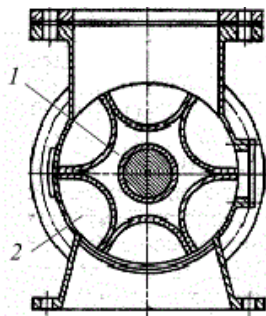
Схема питателя с ячеистым барабаном:
